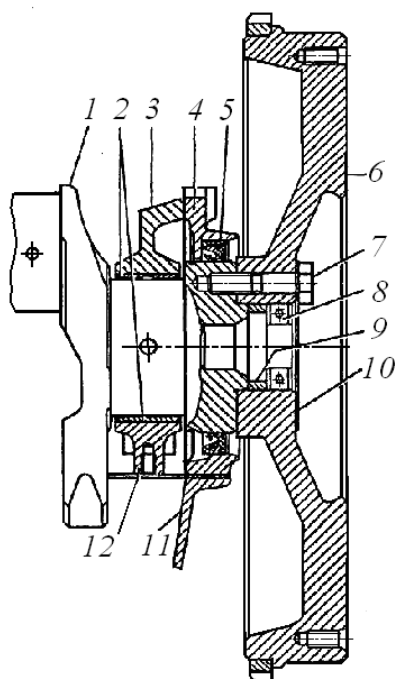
Задний конец коленчатого вала: 1 – коленчатый вал; 2 – вкладыши подшипника; 3 – блок цилиндров; 4 – крышка; 5 – манжета; 6 – маховик; 7 – болт крепления маховика; 8 – подшипник; 9 – распорная втулка; 10 – шайба болтов маховика; 11 – масляный картер; 12 – крышка подшипника
